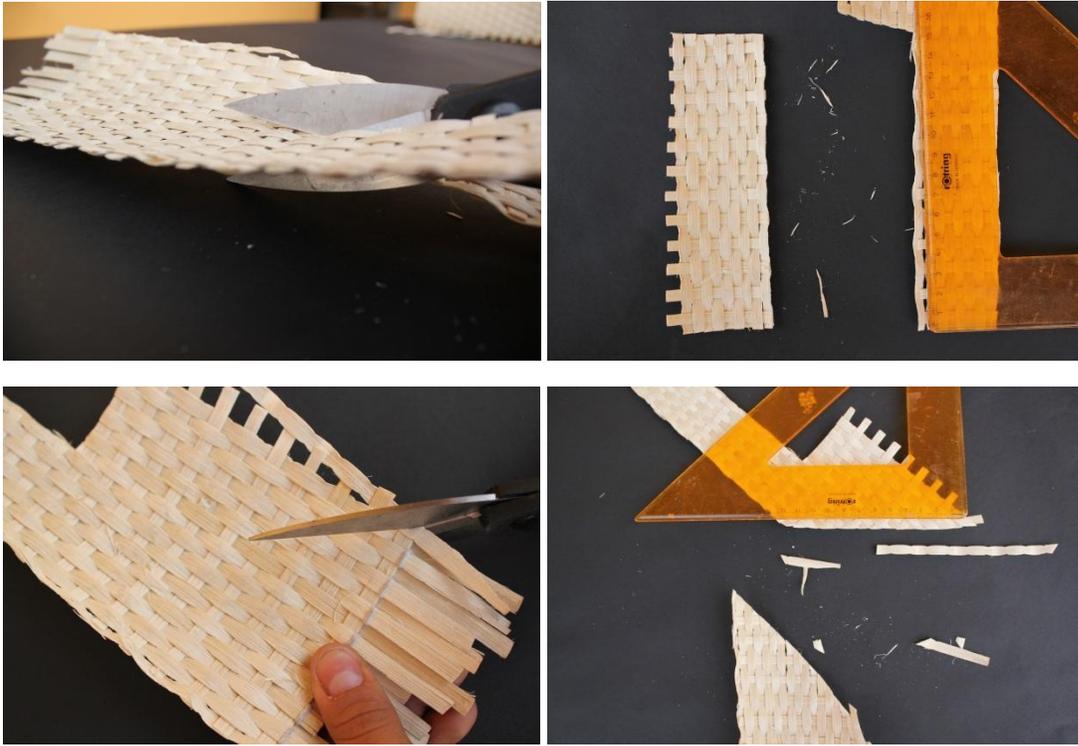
Tipos de Corte y desprendimiento de fibra. Elaboración propia
